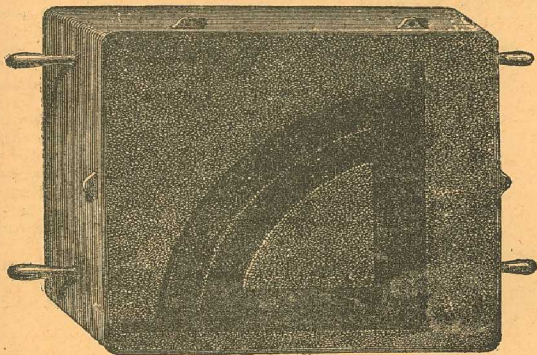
Fundição em caixa, Impressão do modelo, visto de frente.
